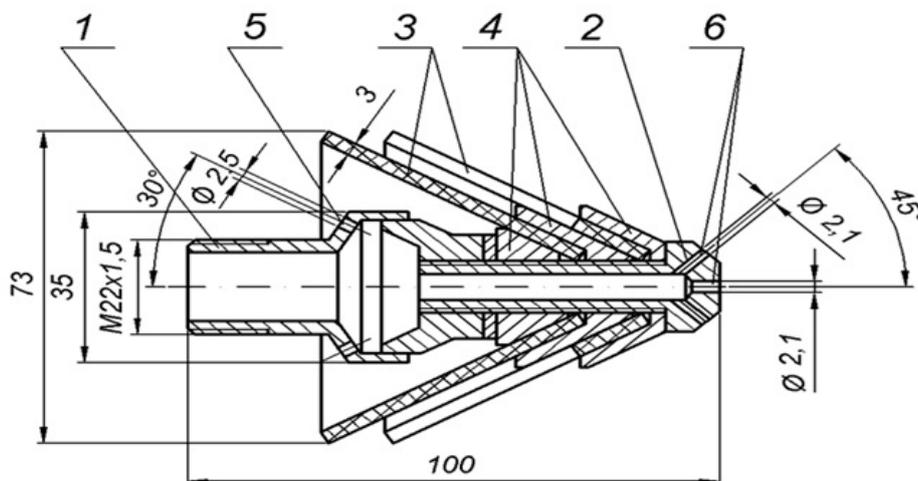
Конструкция насадки промывочной мягкой (НПМ) (патент ВУ11880)
